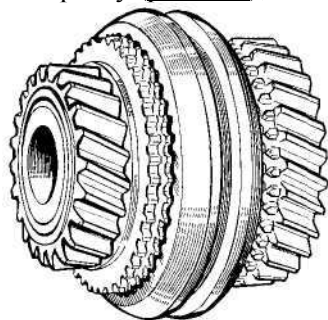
Ступица муфты синхронизаторов III-ей и IV-ой передач с муфтой включения синхронизаторов и набором шестерён (перед установкой в картер коробки передач)
